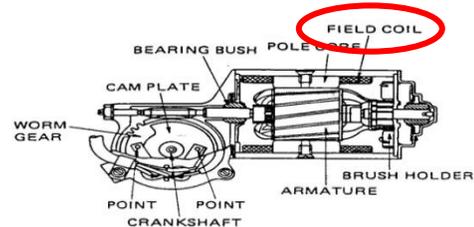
Um "wiper" motor do tipo com estator bobinado ("field coil").
